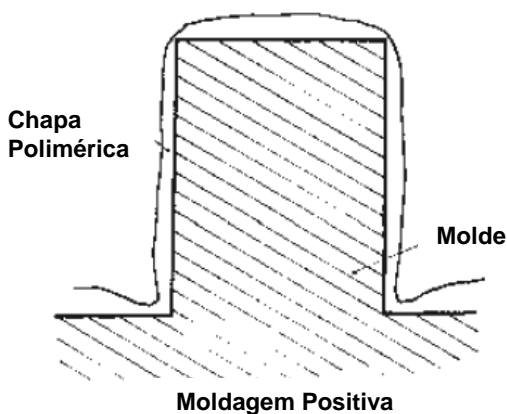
Desenho esquemático para exemplificar a moldagem positiva.
